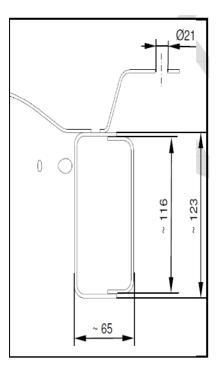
Sezione S-S (Amarok SC/DC)
